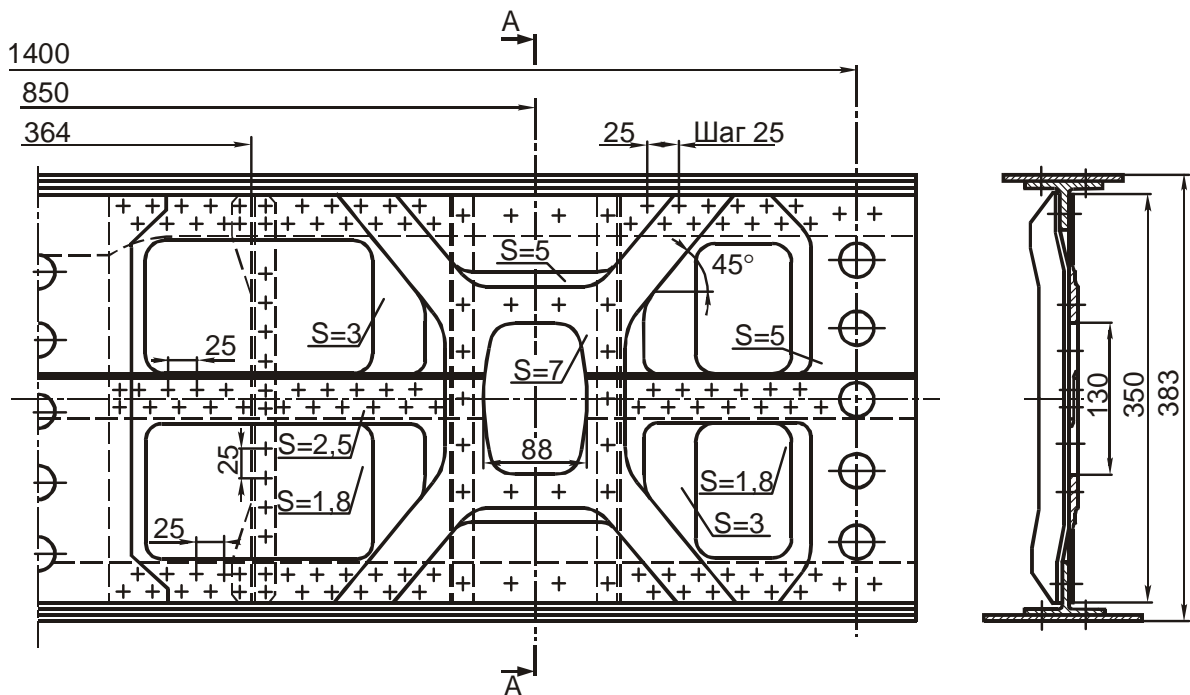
Модель консоли отсека лонжерона с усиленным вырезом в стенке прямоугольной формы со скругленными углами
